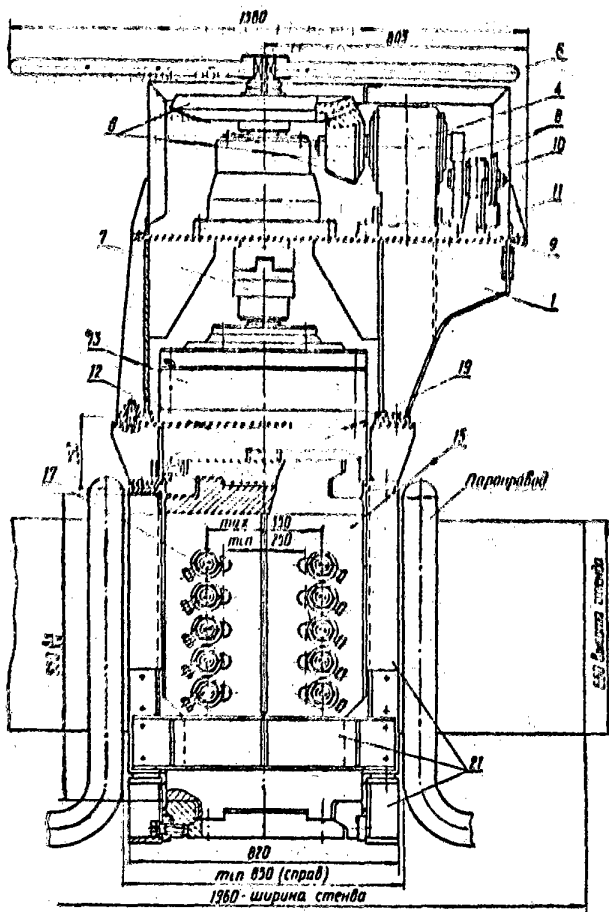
Устройство для плавной передачи усилия натяжения арматуры на бетон (вид спереди)
